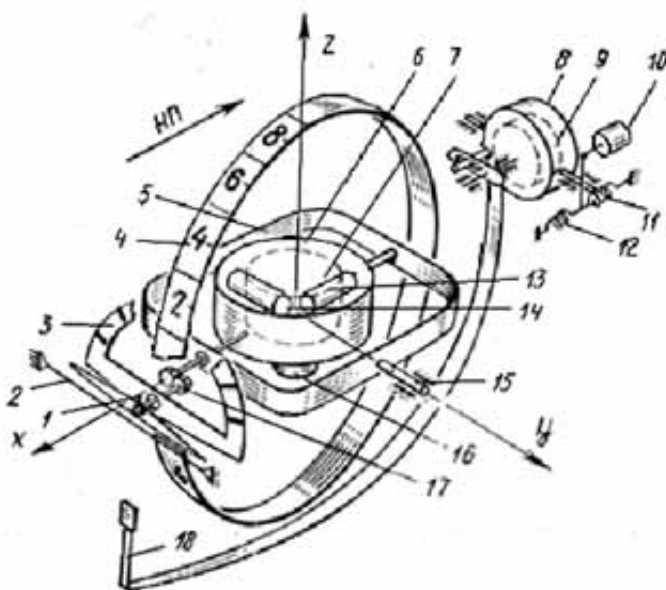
Кинематическая схема авиагоризонта АГК-47Б:
